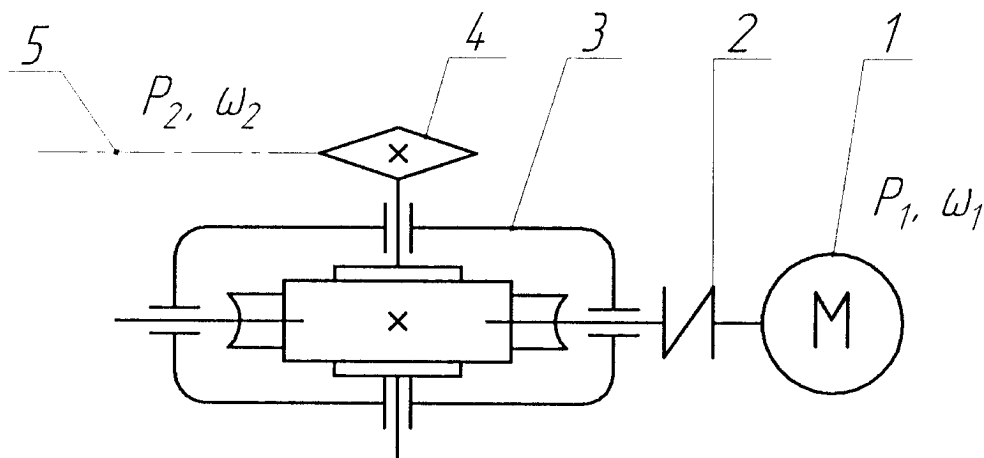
Механічний привод з глобоїдною черв'ячною передачею
